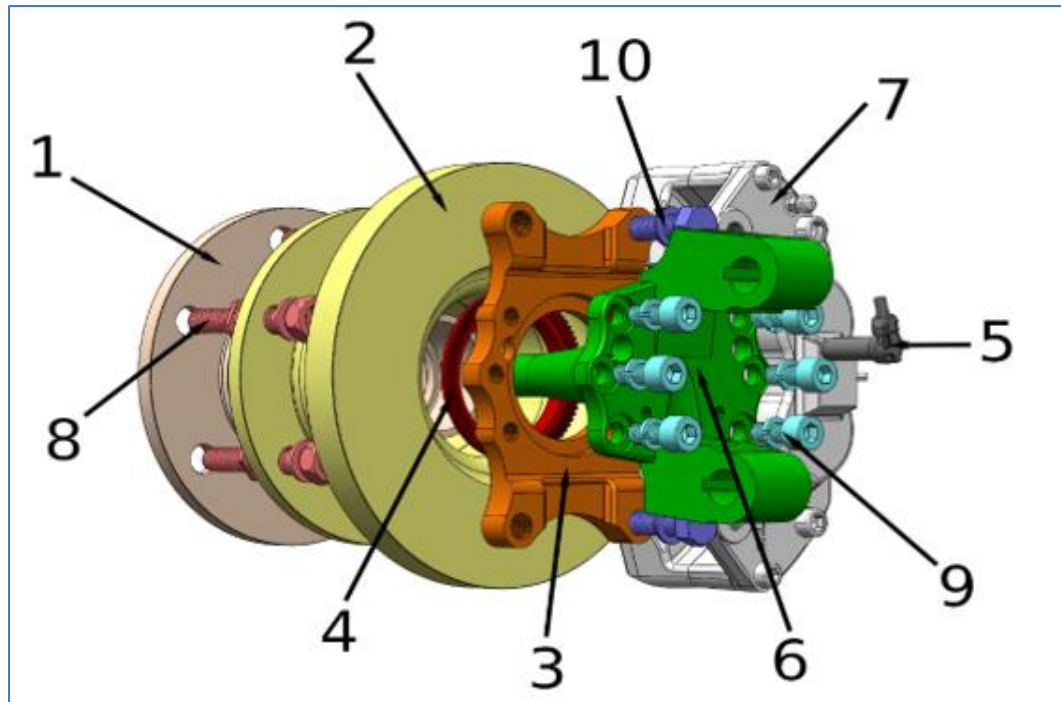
Vue éclatée de l'ensemble frein dessiné avec SolidWorks
